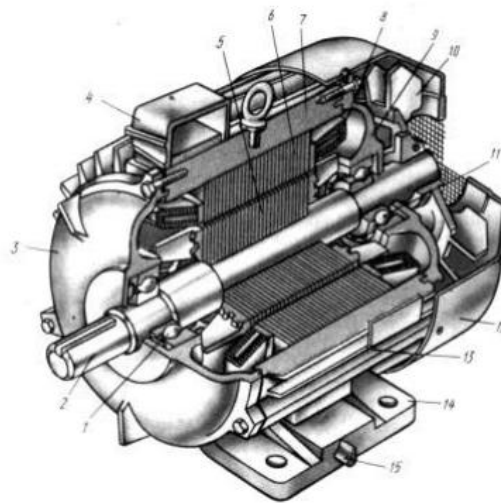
Будова трифазного асинхронного двигуна. 1, 11 – підшипники, 2 – вал, 3, 9 – підшипникові щити, 4 – коробка виводів, 5 – сердечник ротора, 6 – сердечник статора, 7 – корпус статора, 8 – обмотка статора, 10 – вентилятор, 12 – кожух, 13 – ребра, 14 – лапи, 15 – болт заземлення
